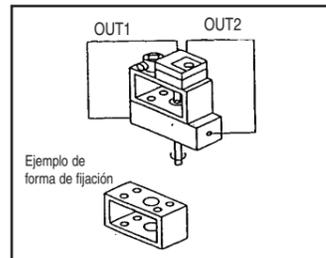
Ejemplo de montaje mediante el tornillo posterior del posicionador
